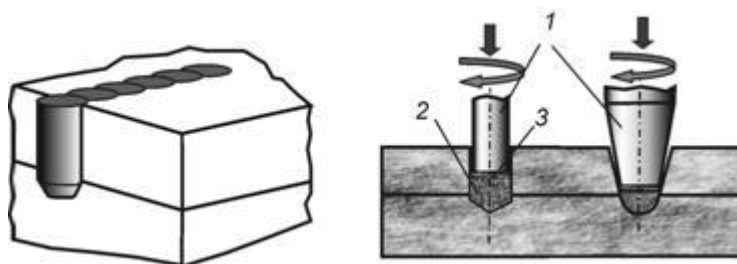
Схема штифтовой сварки трением: 1 – штифты цилиндрической и конической формы; 2 - перенесенный с штифта материал; 3 – зона термопластической деформации.
